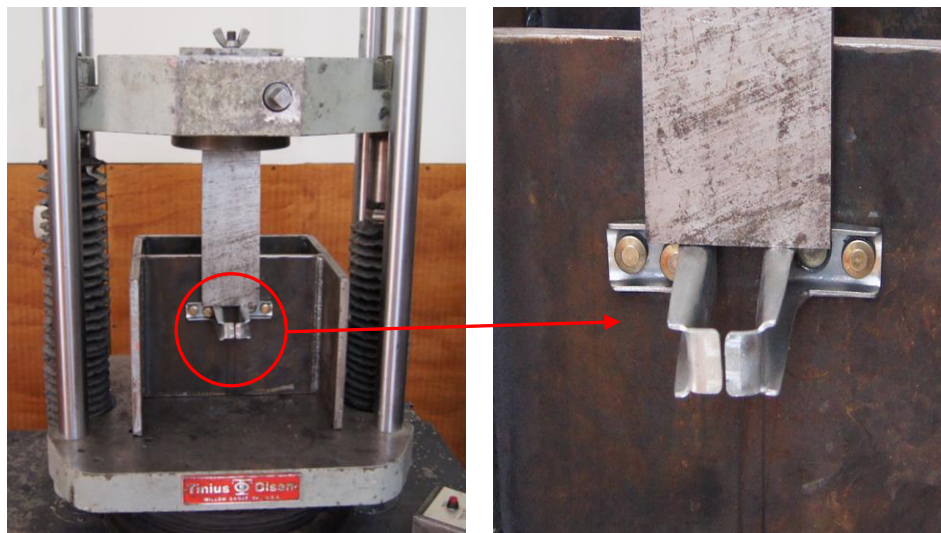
Configuración del ensayo de corte realizado al conjunto.
